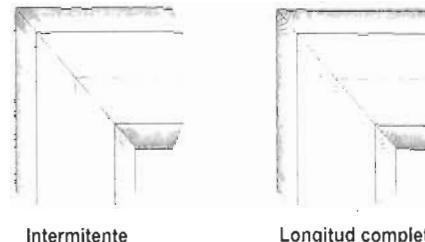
Símbolo de cordón de soldadura mediante Oruga.
